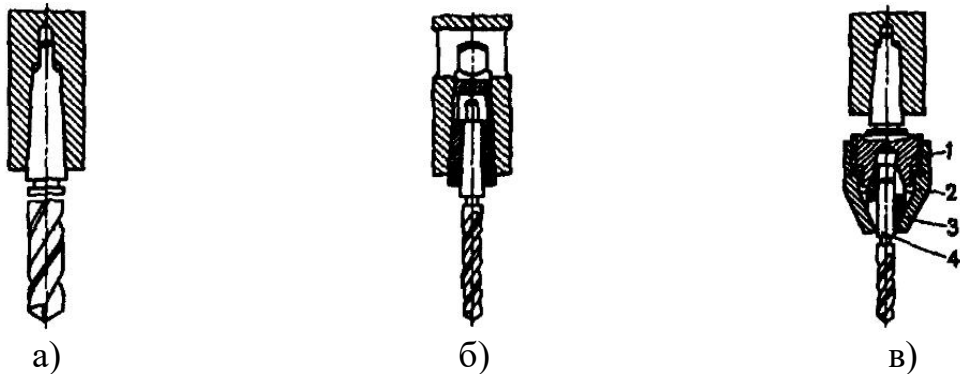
Схеми закріплення інструменту на свердильних верстатах
